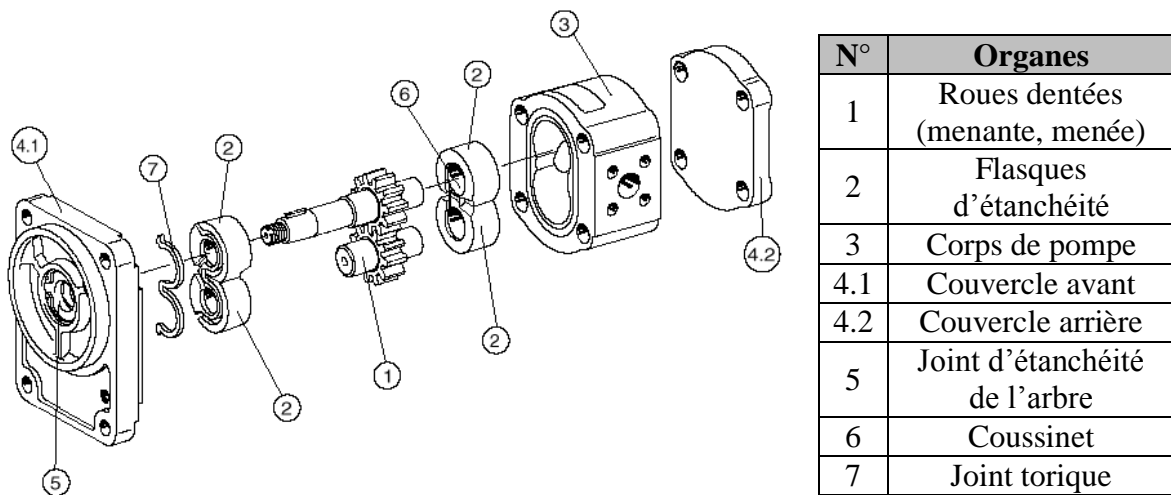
Vue éclatée d'une pompe à engrenage externe (Turbomeca)
